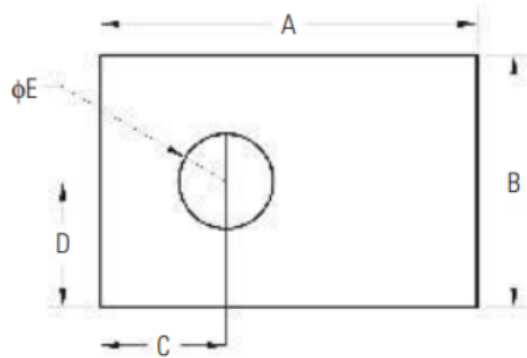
Una tolerancia dimensional es la anchura del intervalo de medidas permitidas para una dimensión, estas tolerancias se aplican a dimensiones de forma (A , B y E) y dimensiones de posición (C y D). Imagen extraída de [7].
